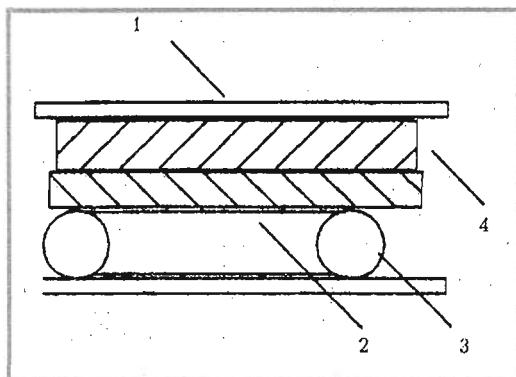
Струбцина с резьбовым стопором и стяжкой: 1 – губки; 2 – стопор с ограничительными гайками; 3 – стягивающая шпилька с гайками; 4 – скрываемые детали
